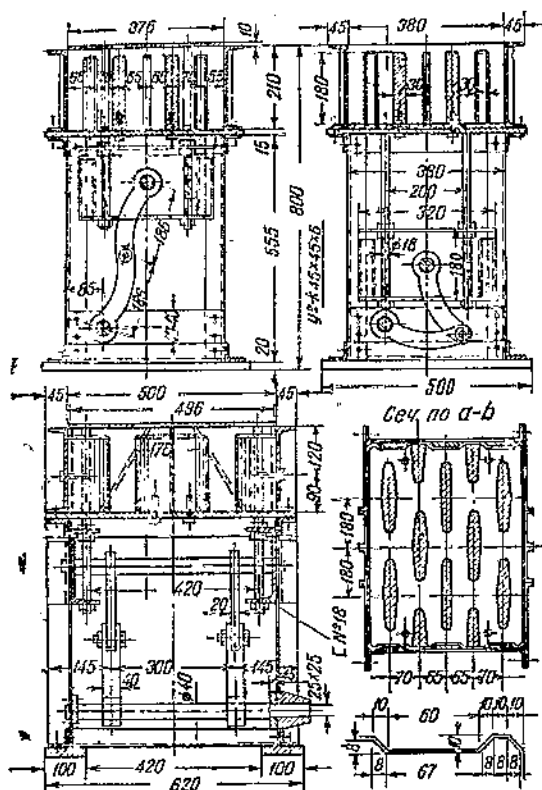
Чертеж станка для блоков „Крестьянин“ размером 50 × 38 × 20 см.
